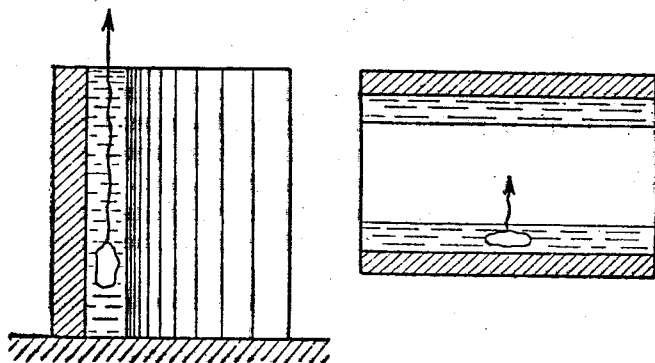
Схема выхода газа при статической и центробежной заливках подшипников
